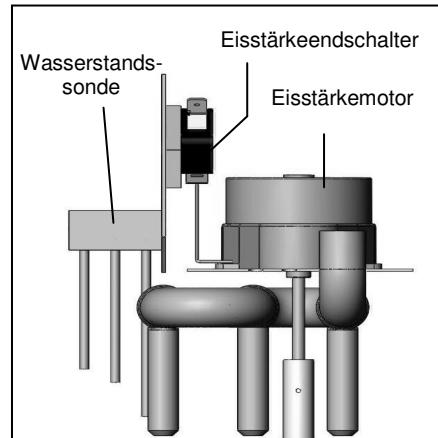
Seitenansicht Eisstärkemotor und Wasserstandssonde
